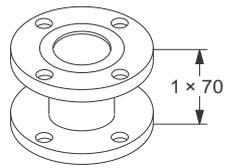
Beispiel für einen Flansch/Flansch-Adapter
